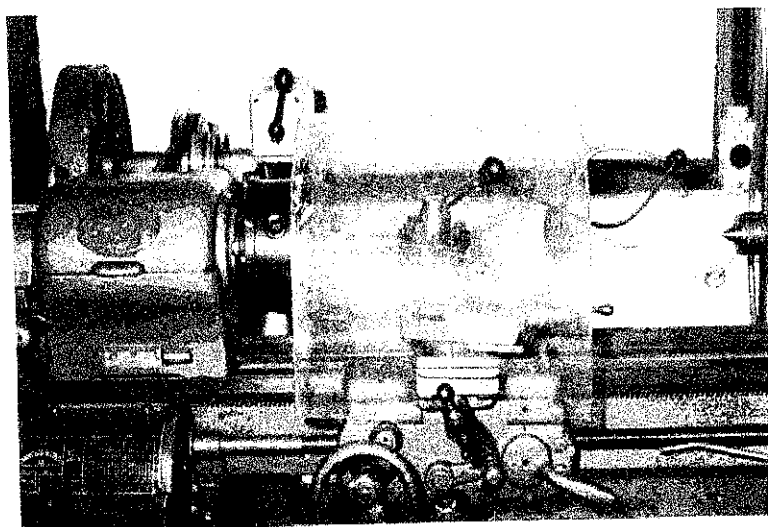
Torno universal para usinagem da barra U-Zr.
